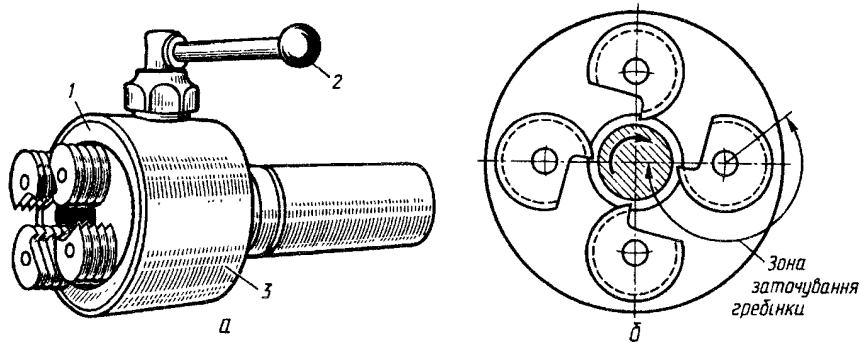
Саморозкривна різьбонарізна головка: а – загальний вигляд; б - схема роботи гребінок: 1 - дискова гребінка; 2 - рукоятка механізму розкривання головки; 3 - корпус
